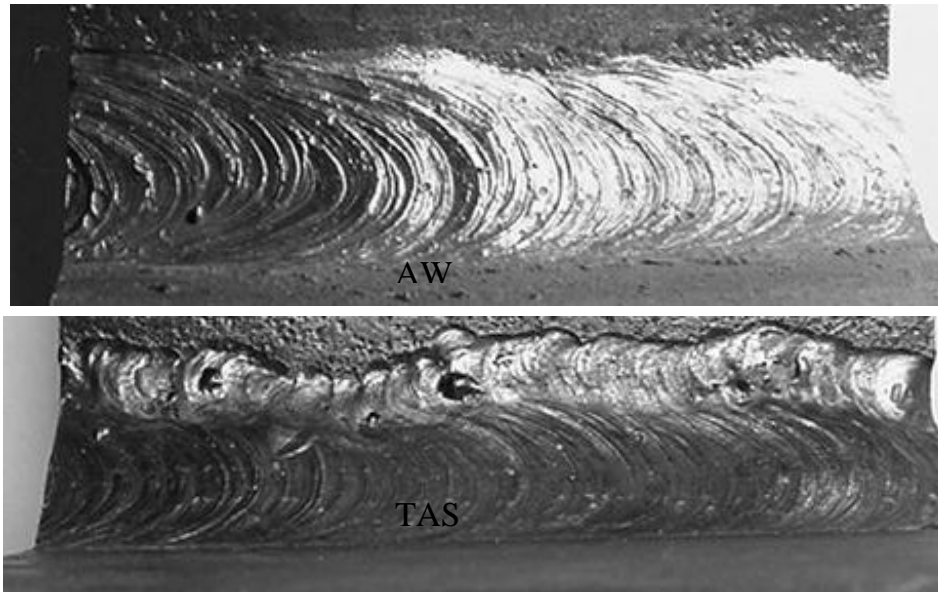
Cordões de soldadura séries AW e TAS.
